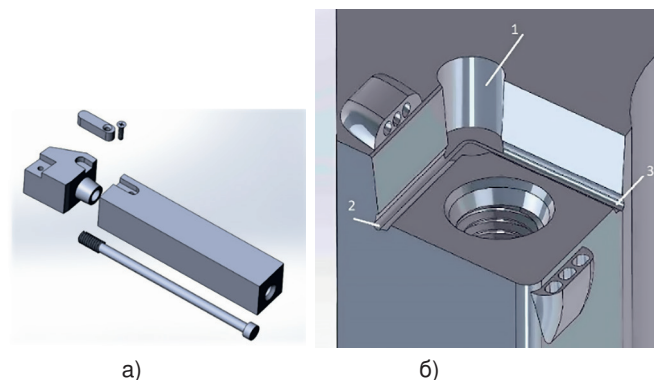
Сборная конструкция державки токарного резца (а) и отверстия для подачи СОЖ на переднюю и заднюю поверхность СМП
